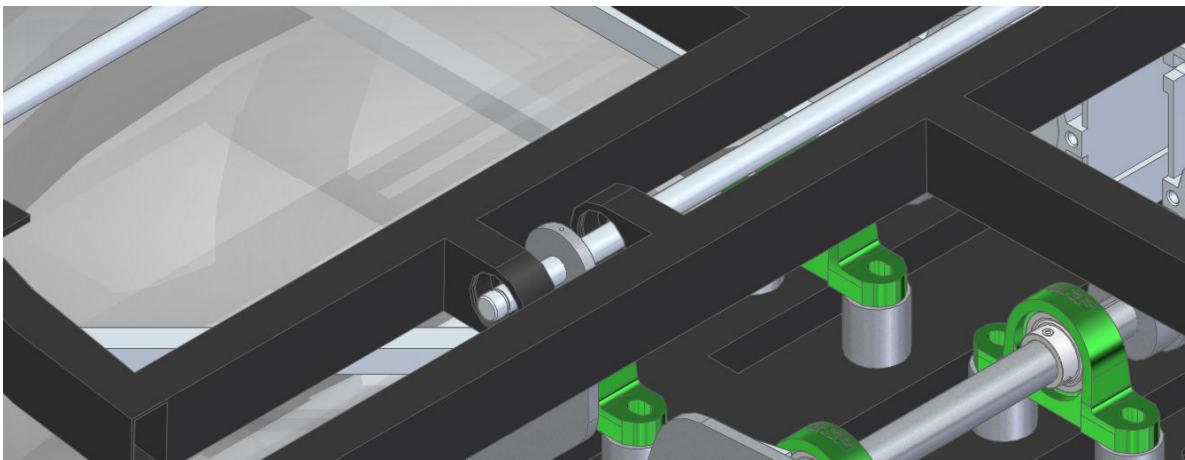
Chumaceras de fabricación especial soldada a los marcos.
